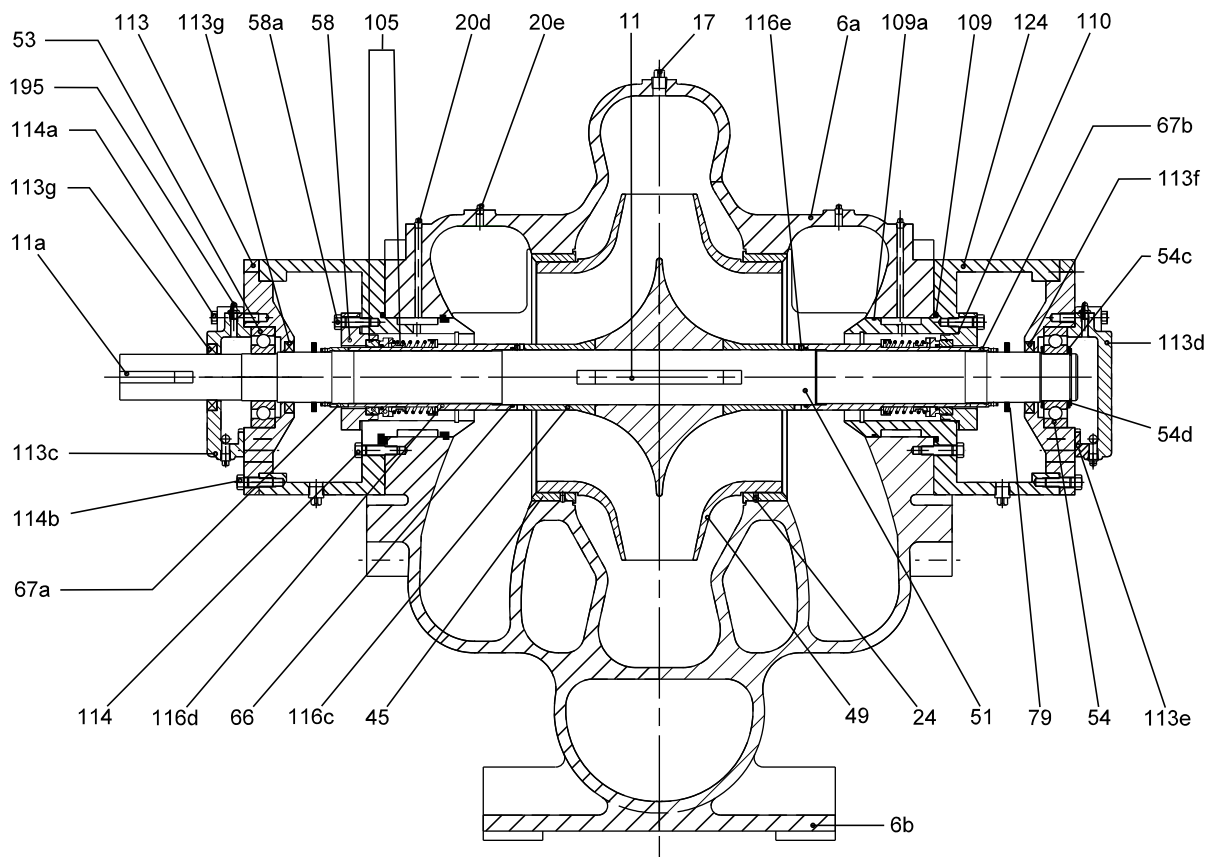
Sección, tipo de construcción 4, con cierres mecánicos del eje
